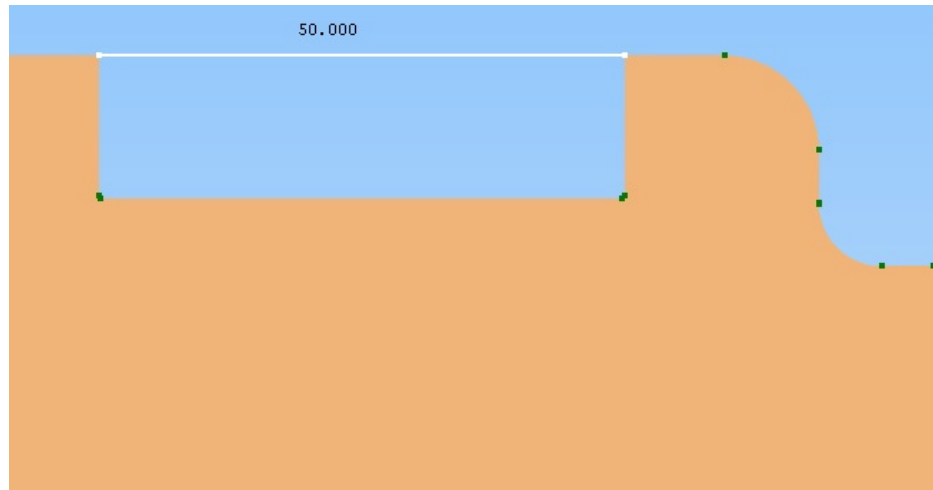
Контроль розміру оброблюваної деталі
